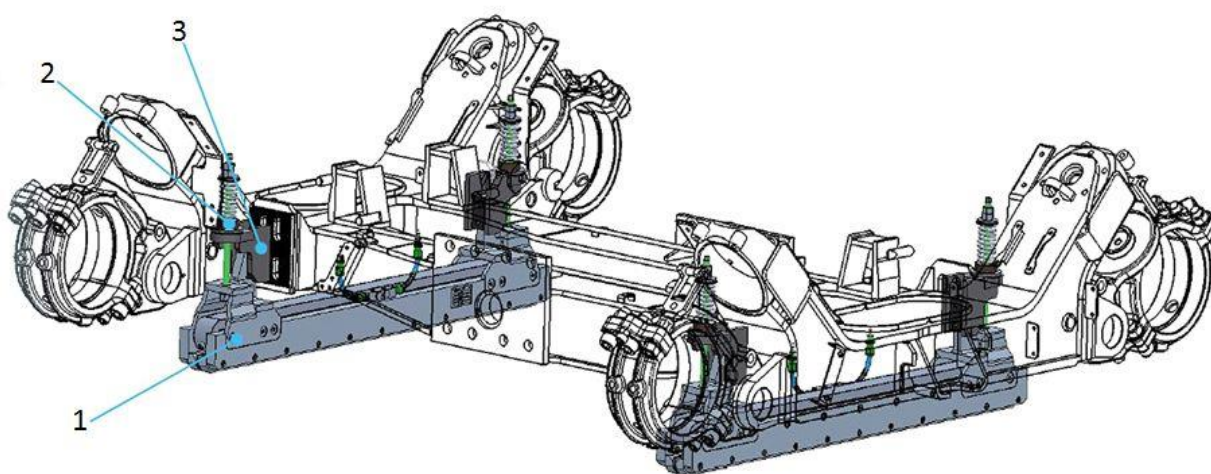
Установка и крепление рельсового тормоза на тележке:
